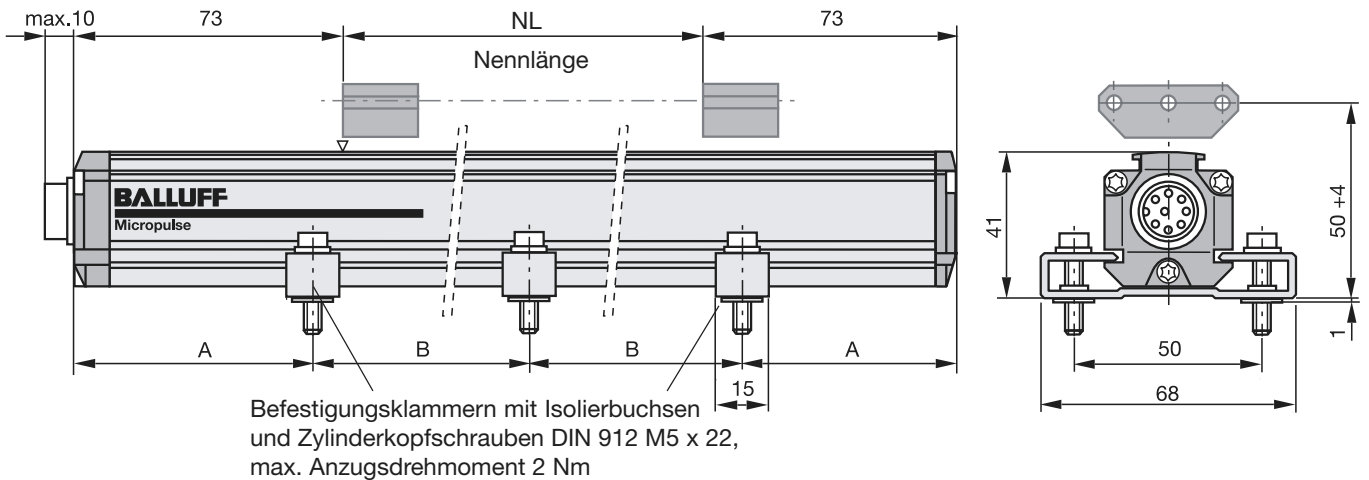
Maßzeichnung (Wegaufnehmer BTL5...P-S32 mit freiem Positionsgeber BTL5-P-3800-2)
